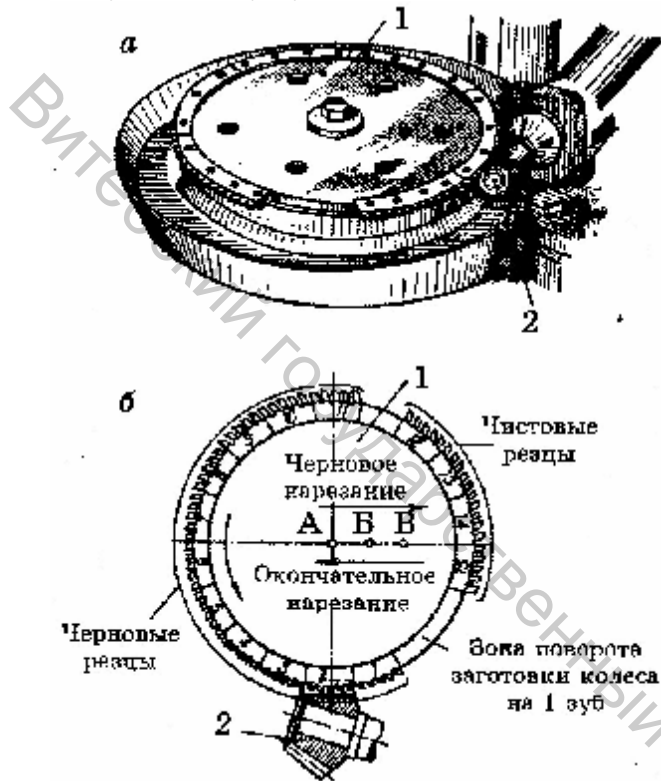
Круговое протягивание зубьев конического зубчатого колеса: 1- круговая протяжка; 2- нарезаемое колесо
